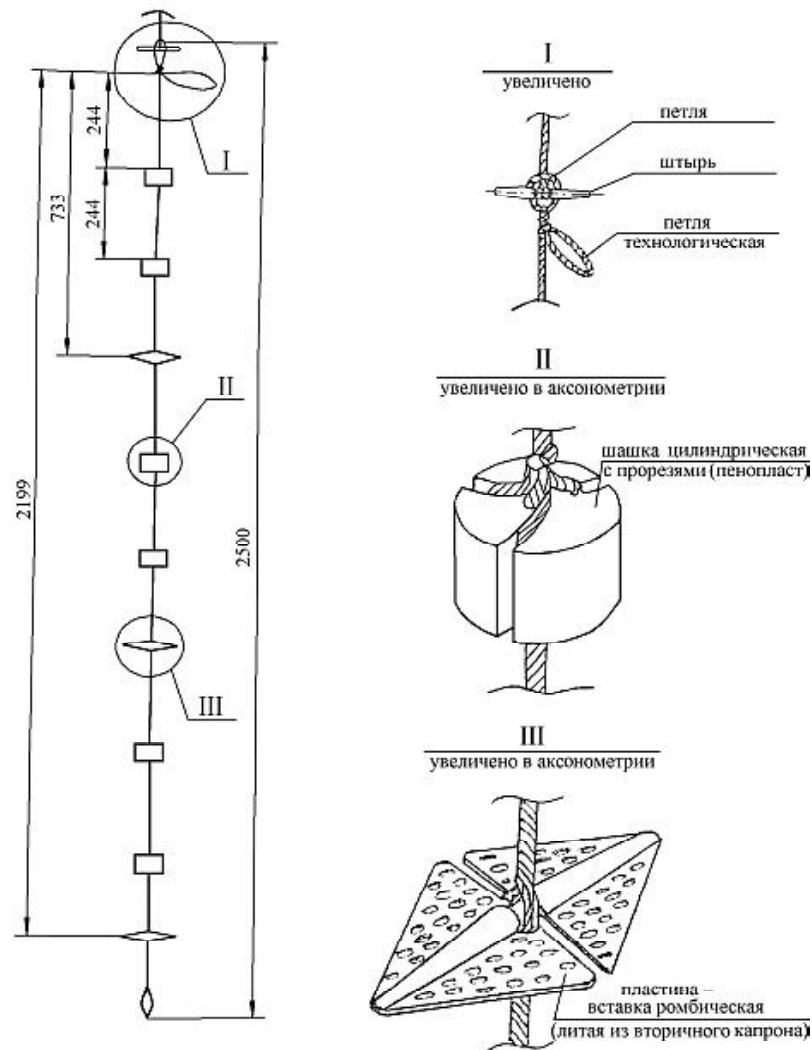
Коллектор «непрерывнопроцессного» типа для сбора личинок и выращивания товарных мидий
